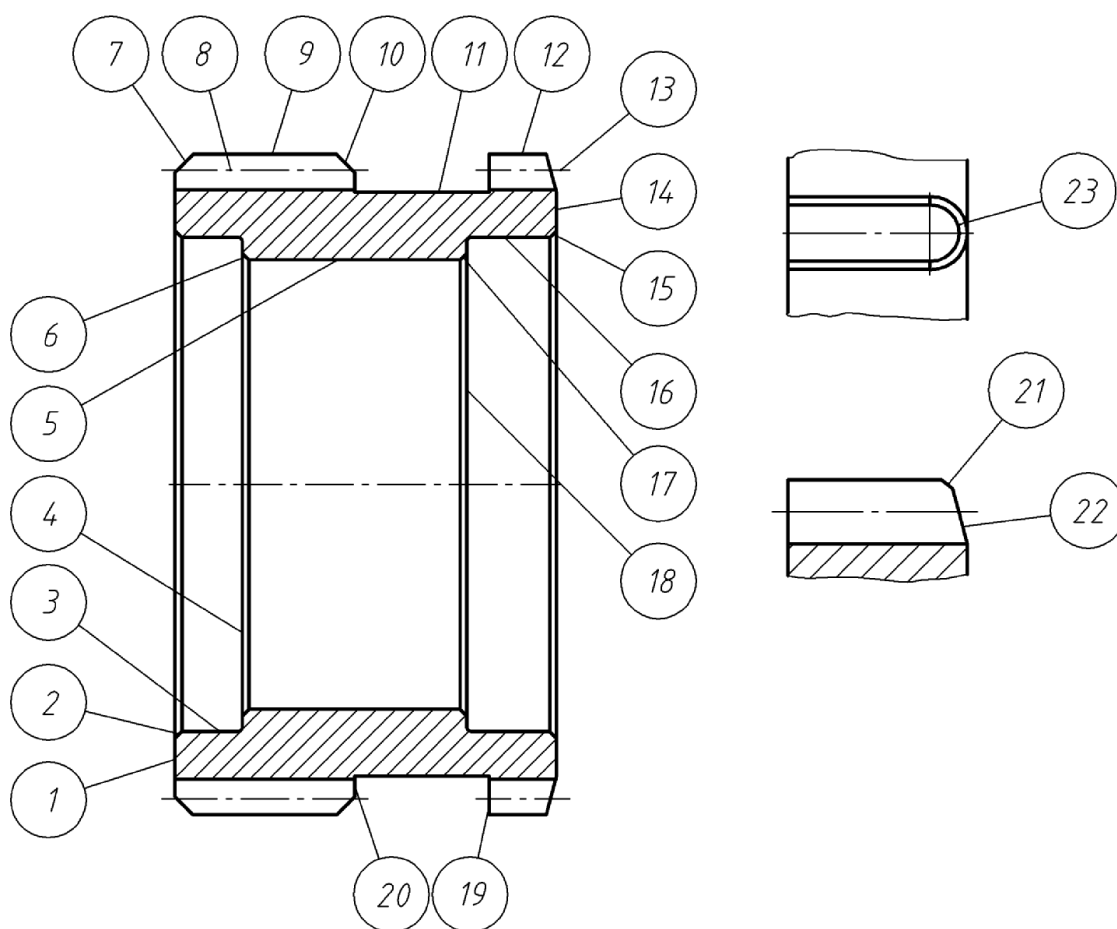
Шестерня, эскиз обрабатываемых поверхностей
